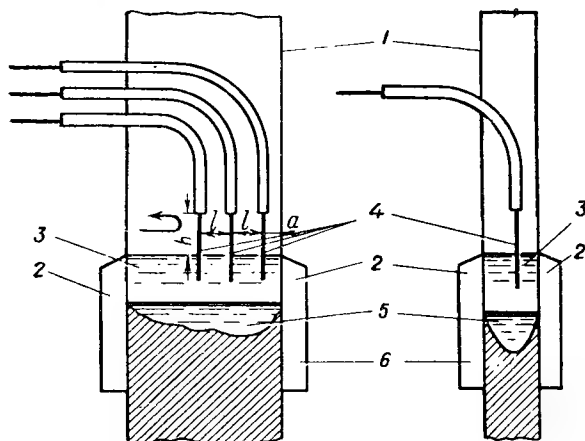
Схема процесса электрошлаковой сварки
